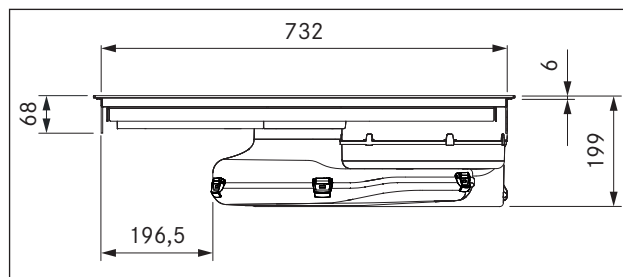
PURU dimensioni apparecchio vista frontale
